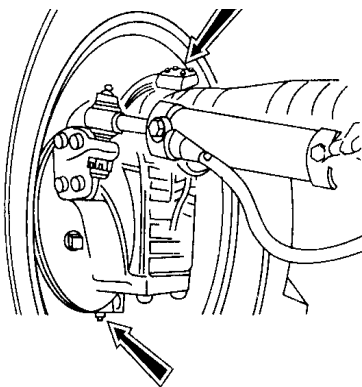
Смазка подшипников опор шкворня колесного редуктора и втулок оси качания ПВМ
